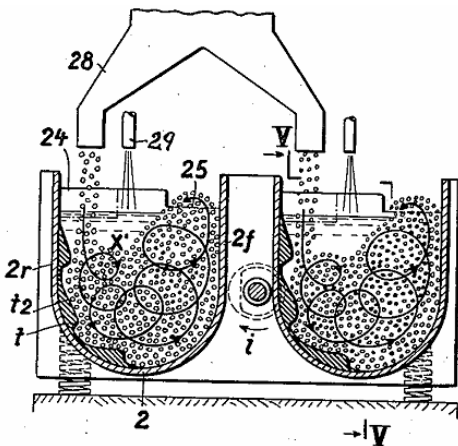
Machine vibratoire avec deux chambres de travail en forme U [48]
